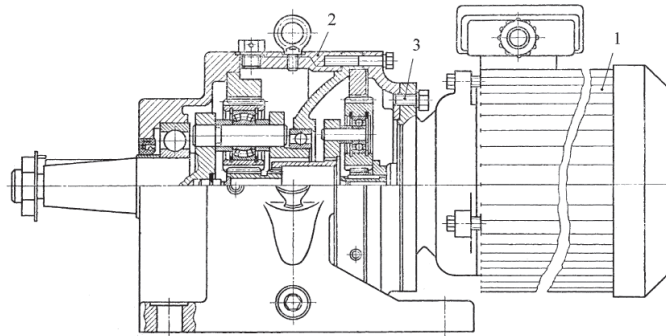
Планетарный двухступенчатый мотор-редуктор
